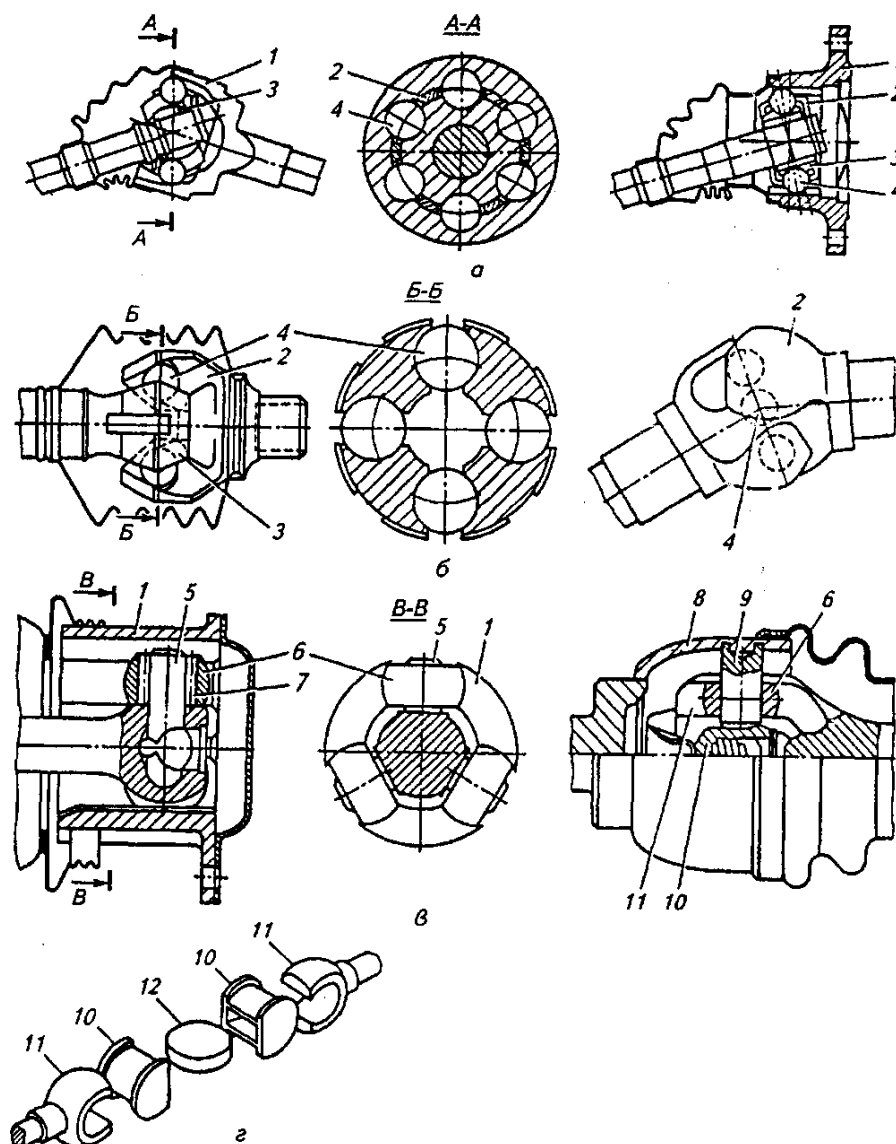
Синхронные шарниры: а - с шестью шариками; б - с пятью и четырьмя шариками; в - трехшпоновые с роликами; г - дисковые; 1 - корпус; 2 - сепаратор; 3 - обойма; 4 - шарик; 5 - трехшпоновая крестовина; 6 - ролик; 7 - игла; 8 - чашка; 9 - шип; 10 - центрирующее устройство; 11 - вилка, 12 - диск
